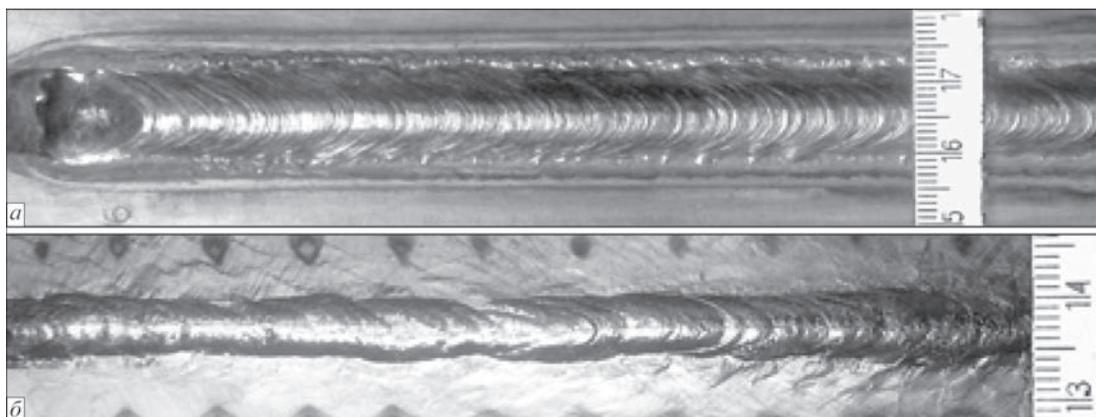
Образец сварного соединения сплава ВТ22 толщиной 8 мм, полученного с использованием присадочной порошковой проволоки ППТ-22: *а* — лицевая поверхность сварного шва; *б* — обратное формирование
